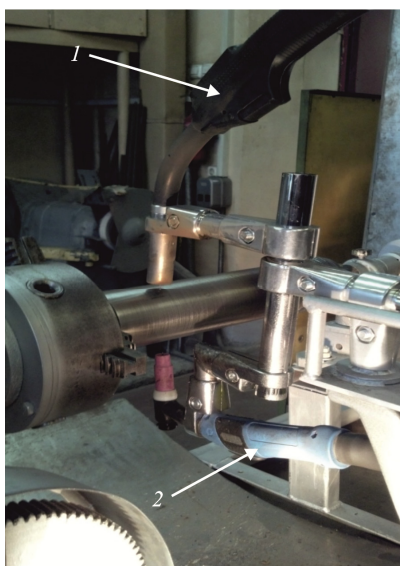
Расположение горелок: 1 – сварочная горелка механизированной сварки в смеси газов; 2 – сварочная горелка с неплавящимся электродом в аргоне
